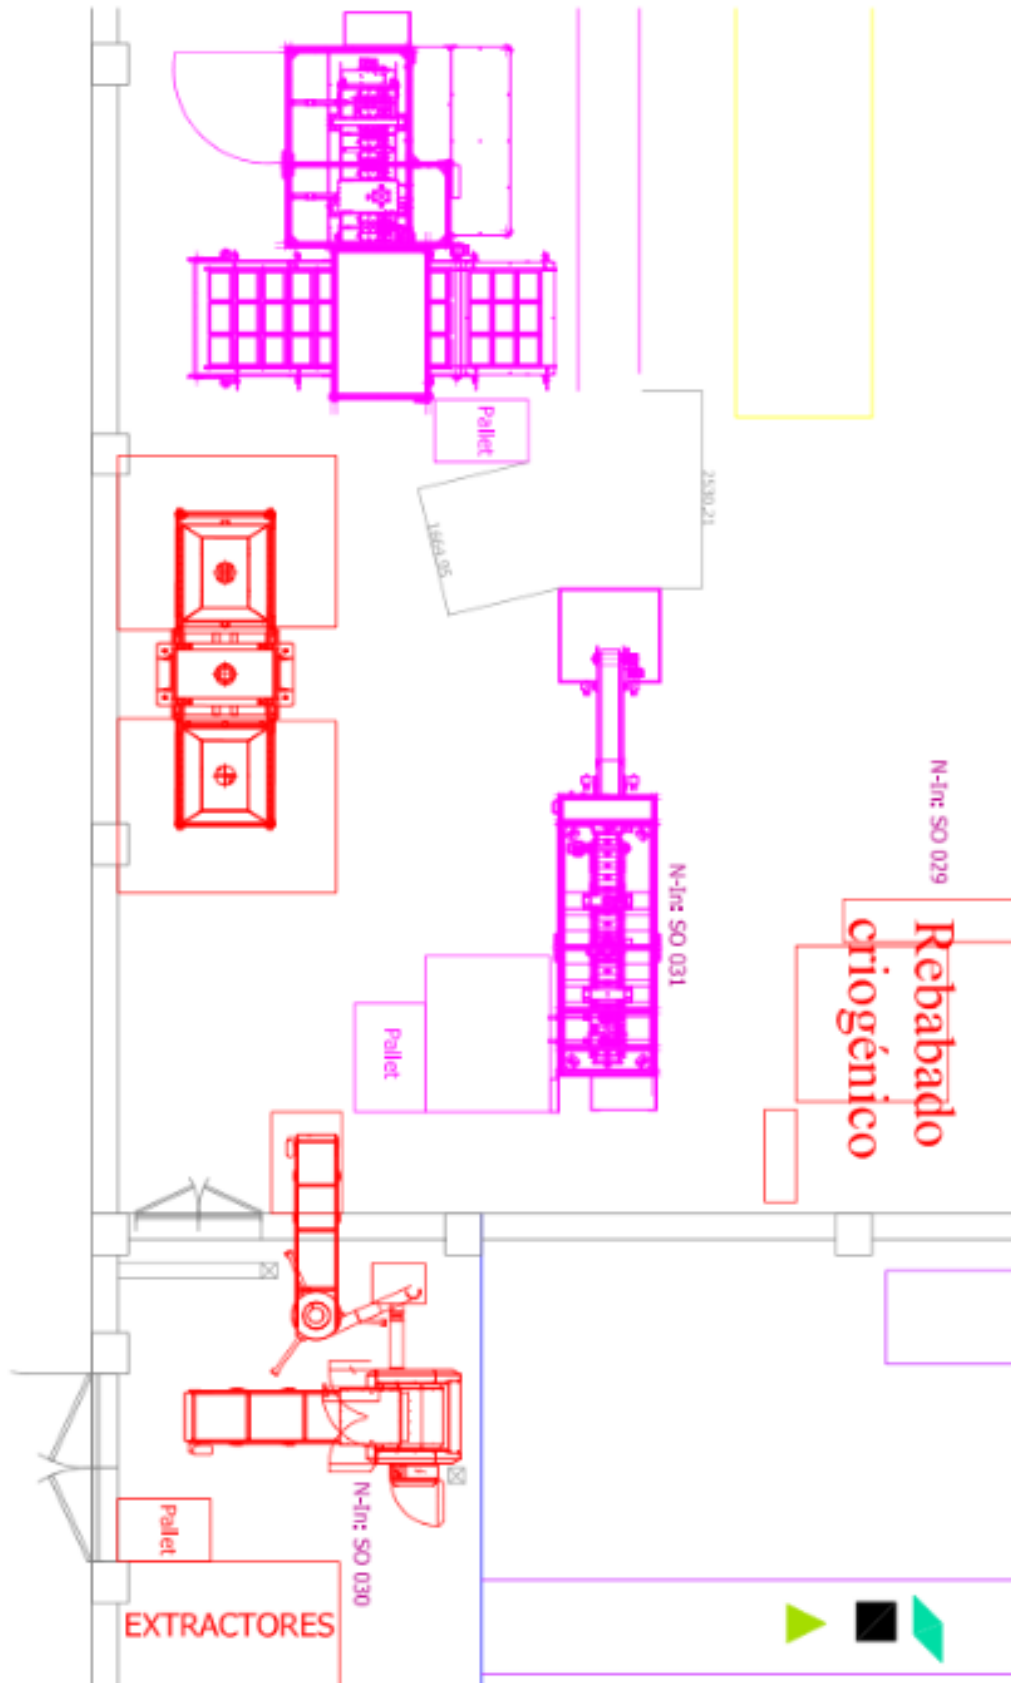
Distribución en planta propuesta para el equipo necesario.
